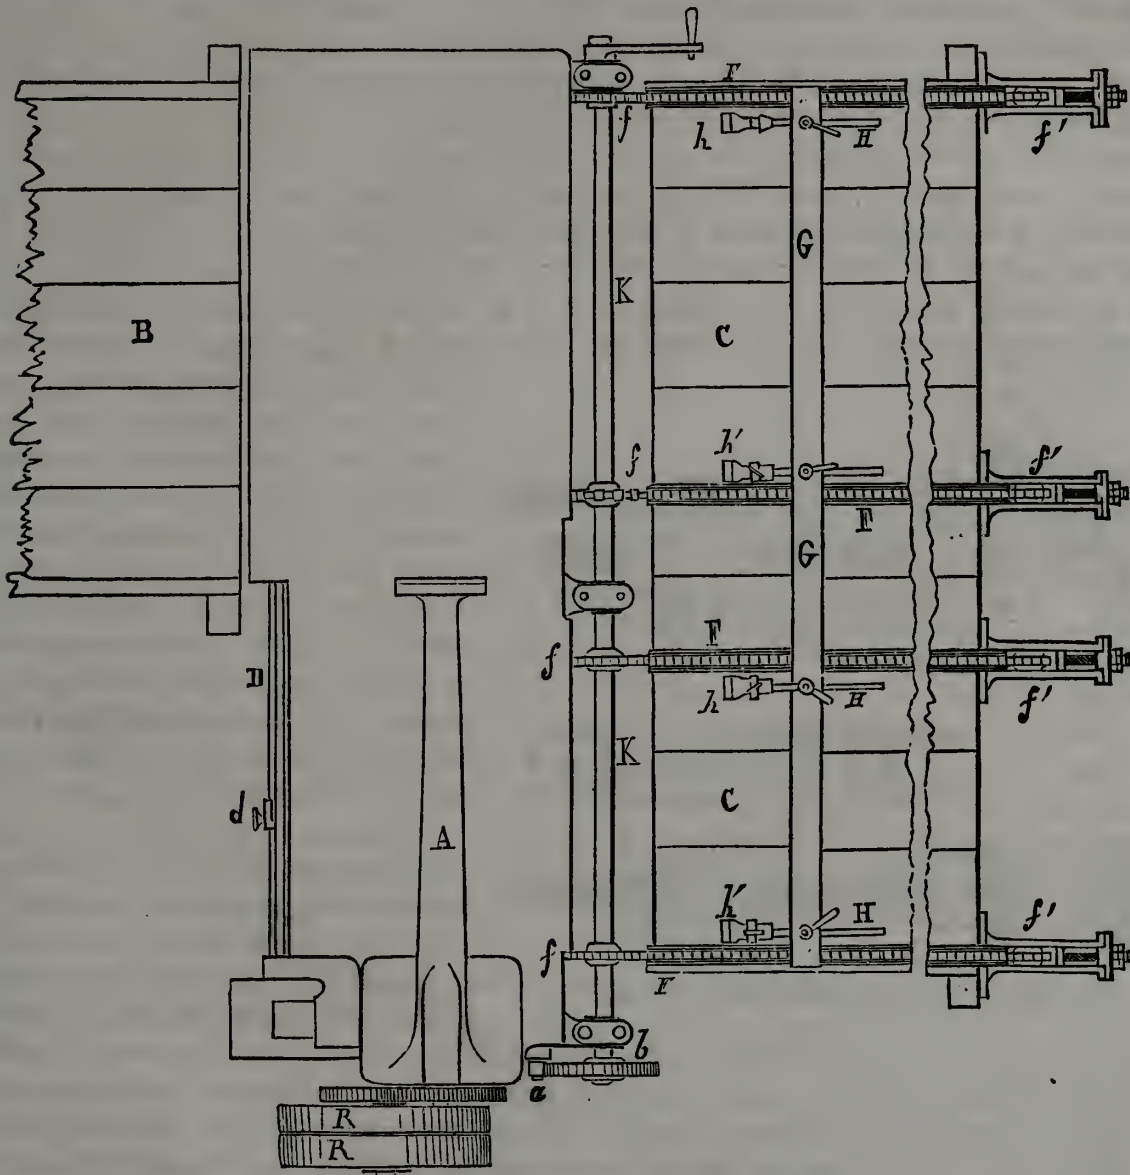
Machine à coudre les voiles de M. Coignard.
